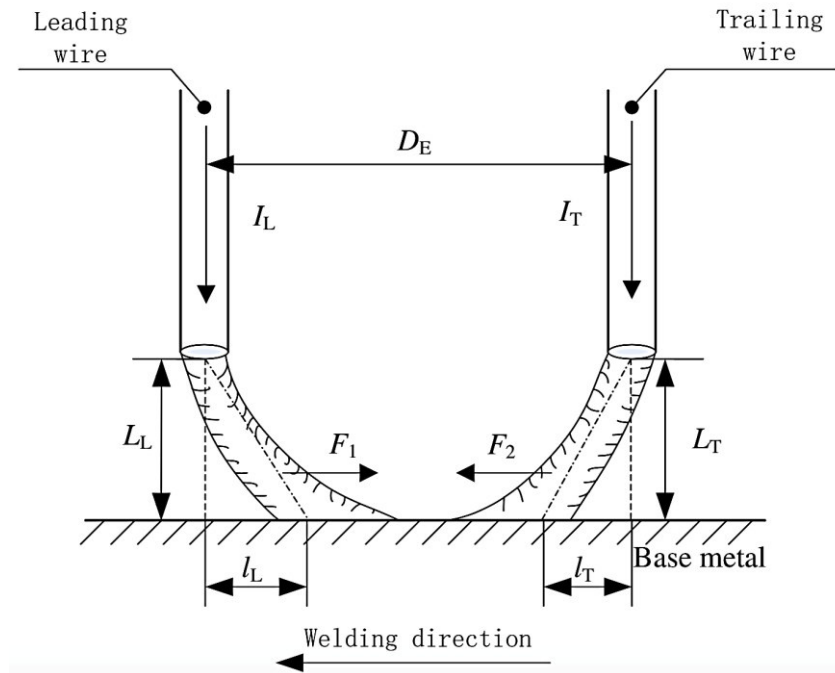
Representação do fenômeno de deflexão de arcos no processo de soldagem tandem GMAW [24].
